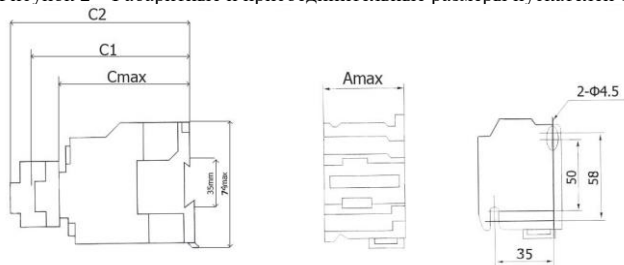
Габаритные и присоединительные размеры пускателей 16-40А
